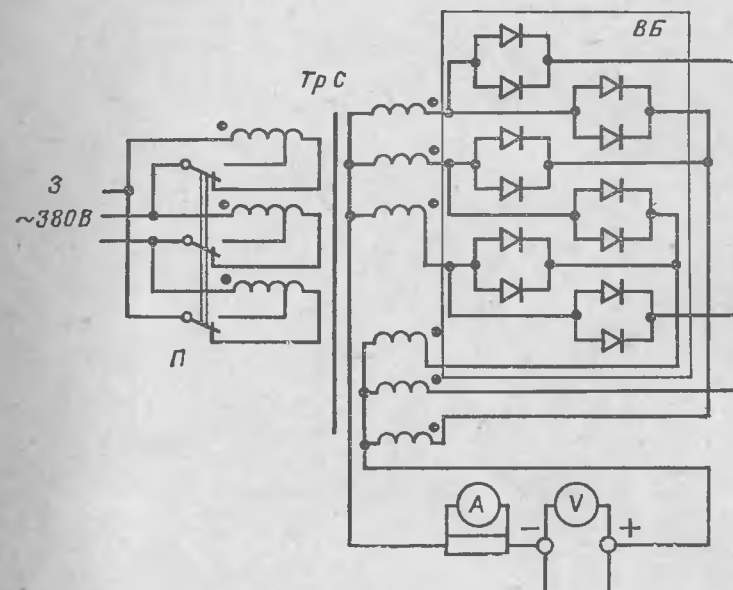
Электрическая схема силовых блоков сварочного выпрямителя ВКСМ-1000.
